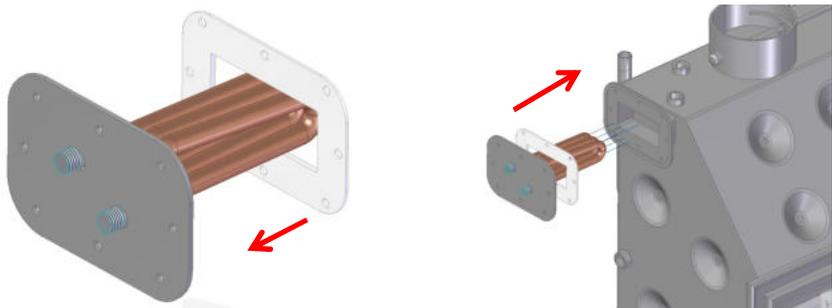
Colocación de la junta en el serpentín y montaje en el equipo
